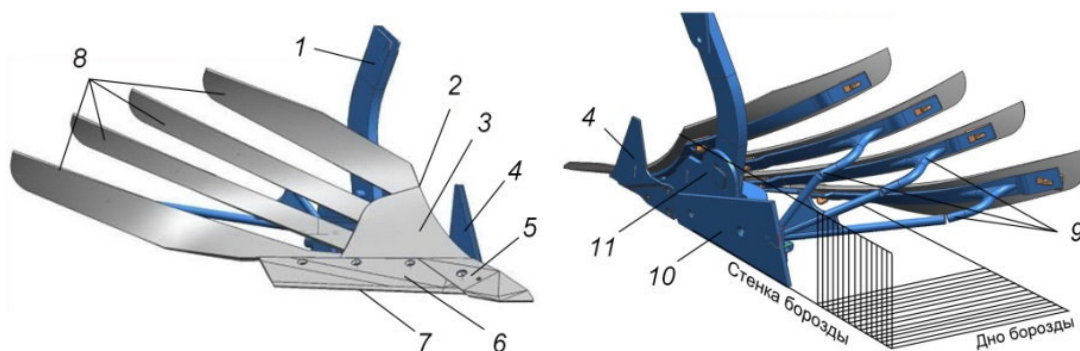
Корпус плуга в сборе со стойкой: 1 – стойка; 2 – полевой обрез;
